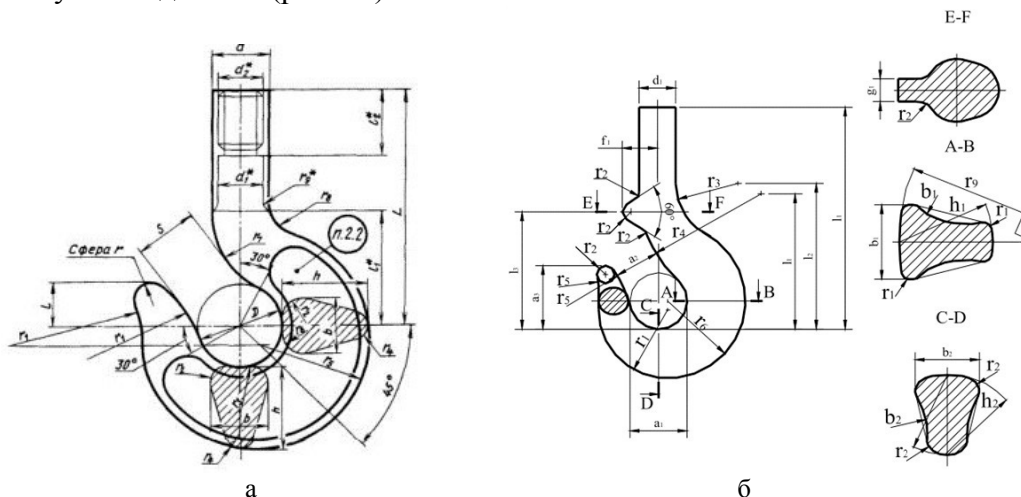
Форми перерізів гаків: а – гак ГОСТ 6627-74 (заготовка); б – гак DIN 15401 форми RSN
